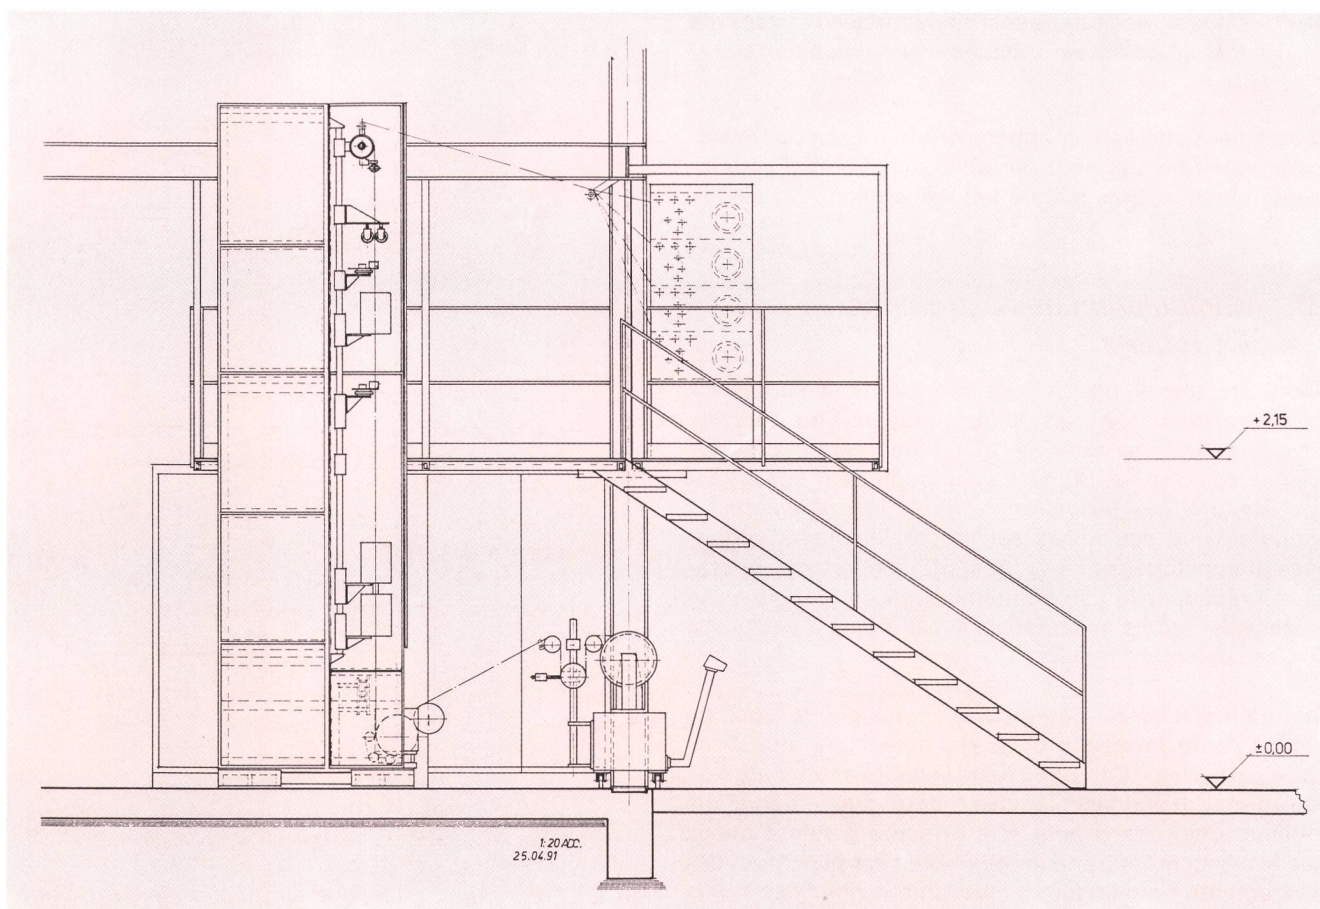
Vue d'ensemble de la ligne de production pilote de rubans de fibres optiques installée à Cabloptic
